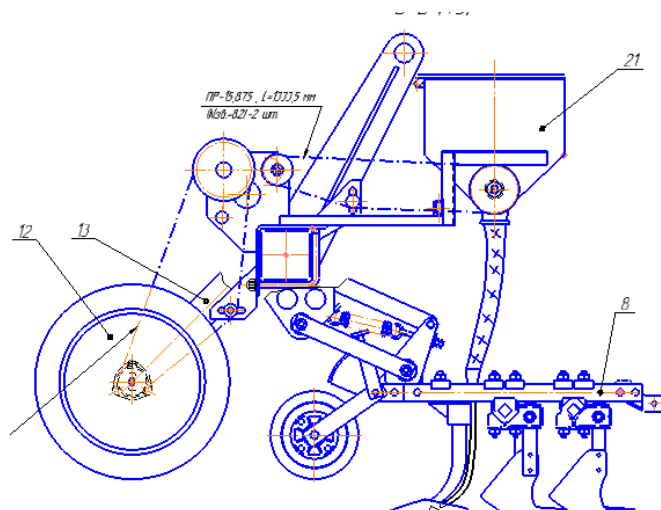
Загальний вигляд і принципова схема культиватора УСМК-8,1
